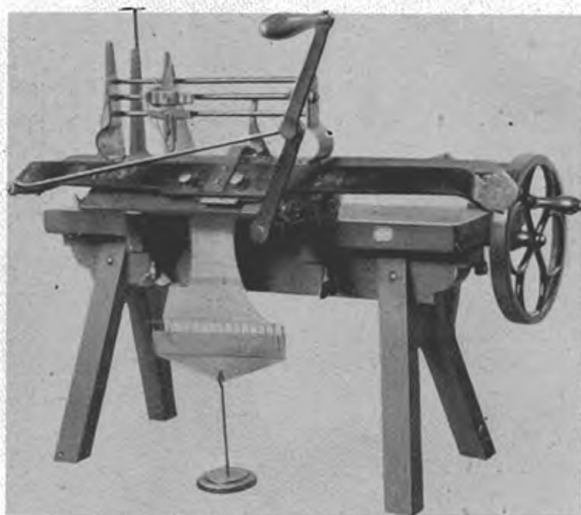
Machine à tricoter J.-W. Lamb (7.793).
